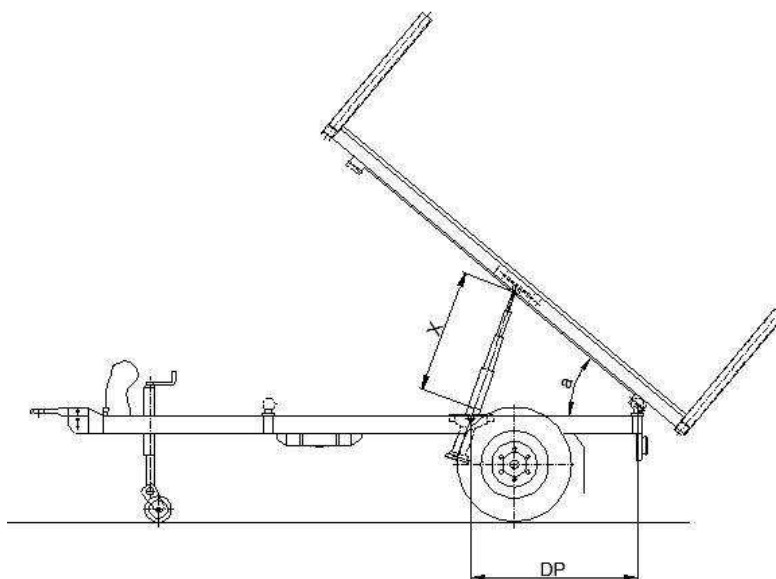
Zobrazení spojitého zatížení – dimenzování pístnice [11]
